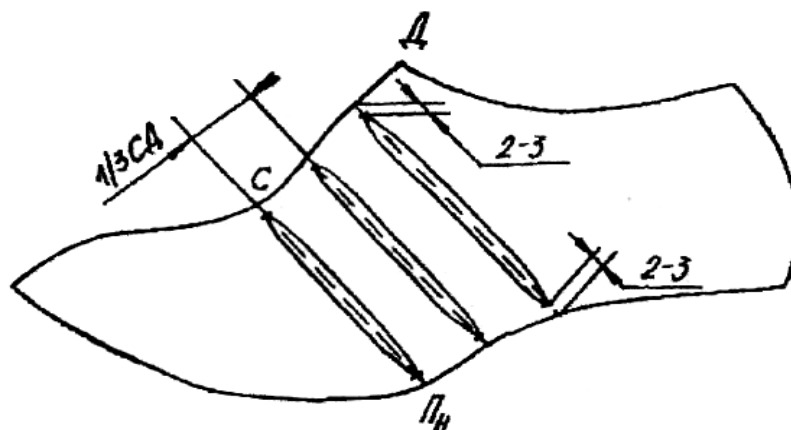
Розрізування зліпку бокової поверхні колодки
